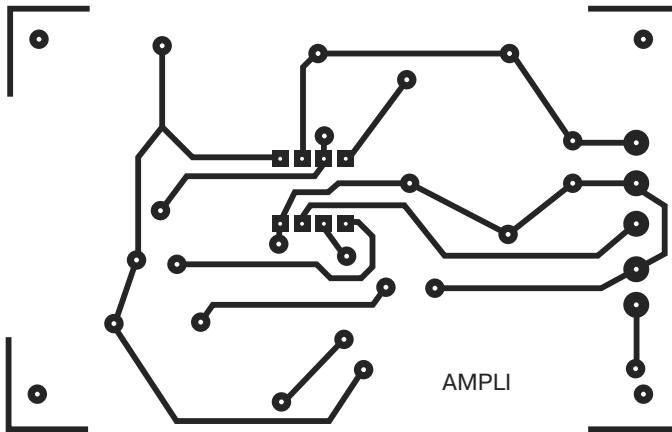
Чертеж печатной платы низкочастотного усилителя
